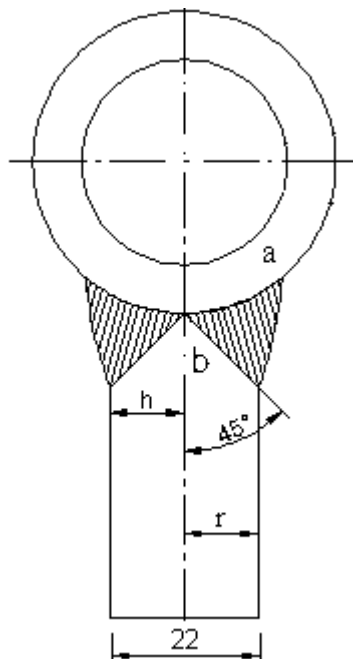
Configuración y unión por soldadura de la cabeza de articulación.
